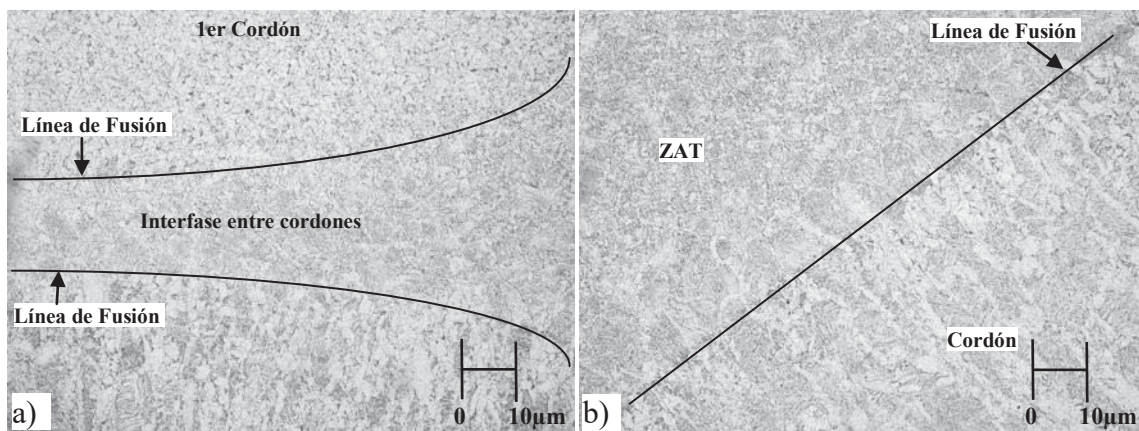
Probetas API 5LX60, con campo magnético 1.8 mT, atacadas con nital al 5%. a) Fotografía de la intersección de unión de los cordones de soldadura. b) Fotografía del cordón de soldadura inferior izquierdo.
